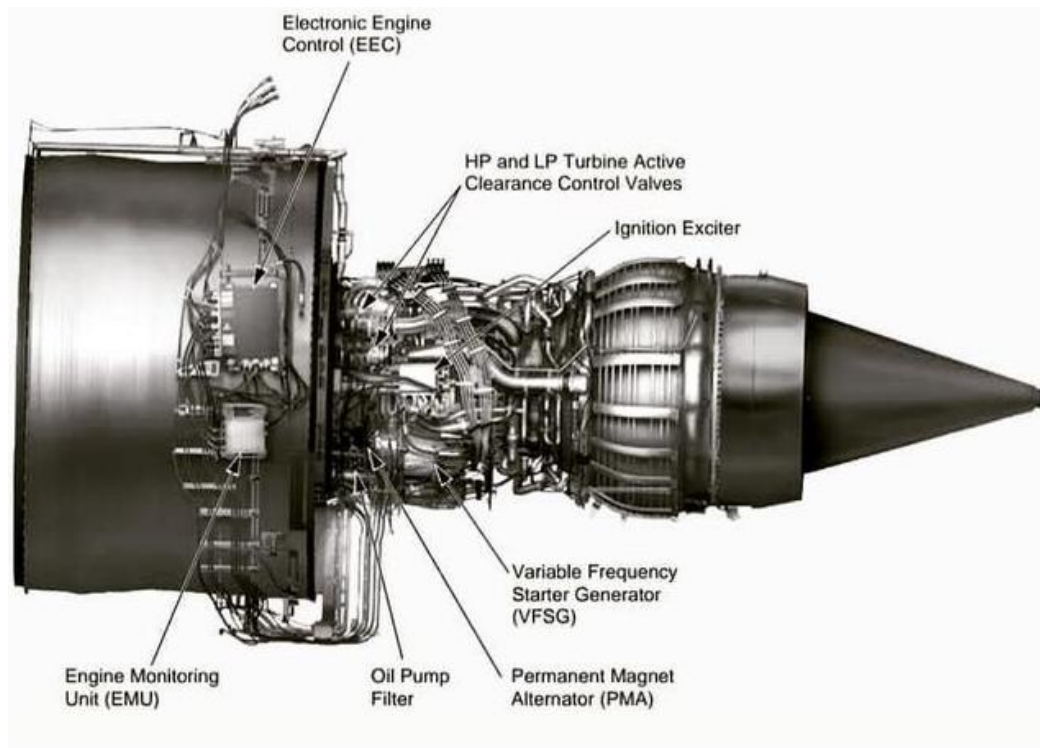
Motor GEnX. Adaptado de [20] y [21].
